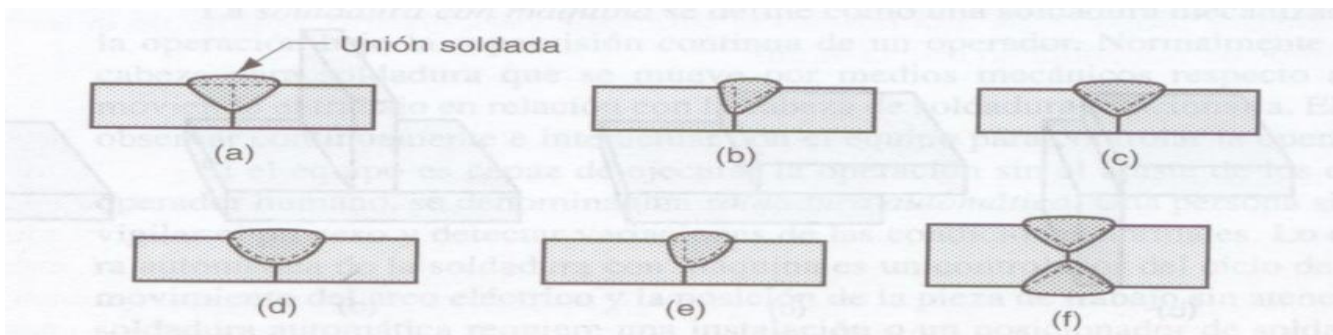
Algunas soldaduras con surco típicas: (a) soldadura con surco cuadrada, un lado; (b) soldadura con surco en bisel único; (c) soldadura con surco en V único; (d) soldadura con surco en U único; (e) soldadura con surco en J único; (f) soldadura con surco en V doble para secciones más gruesas.
